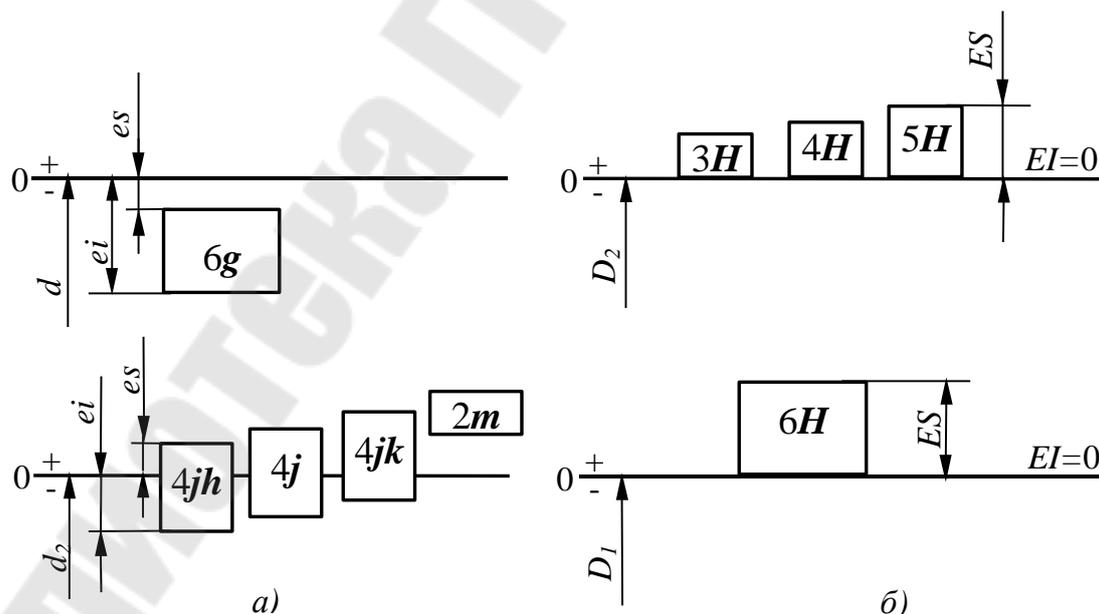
Схемы расположения полей допусков метрической резьбы с переходными посадками: а – для наружной; б – для внутренней.
